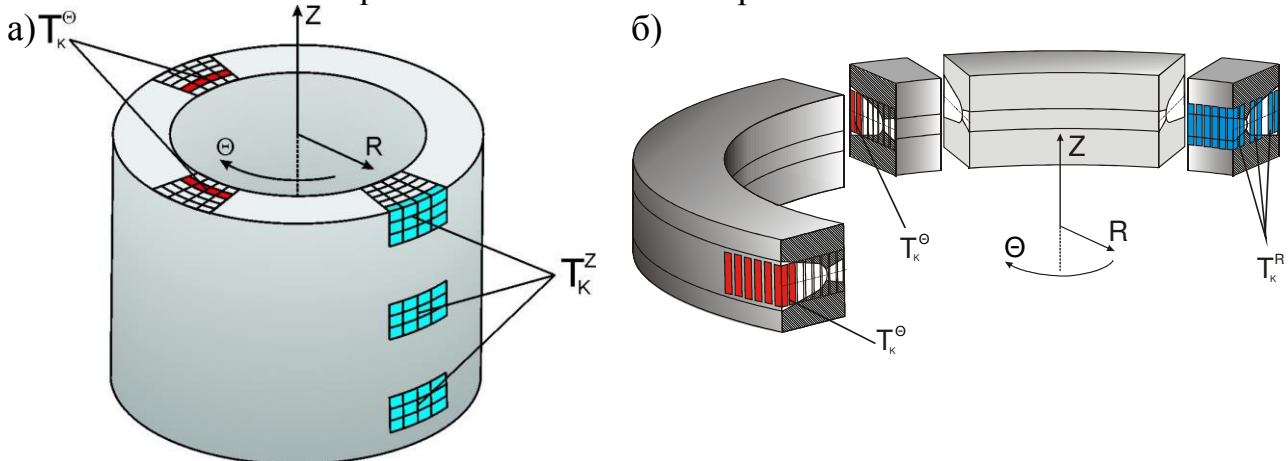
Обозначение системы координат и схемы вырезки образцов из основного металла (а) и металла сварного шва (б).
